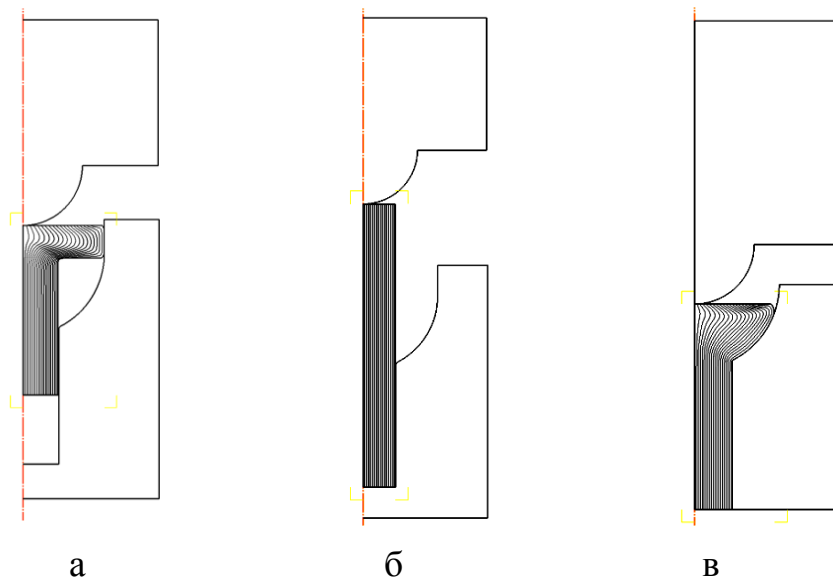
Схеми штампування поковок типу стрижня з напівсферичним фланцем
